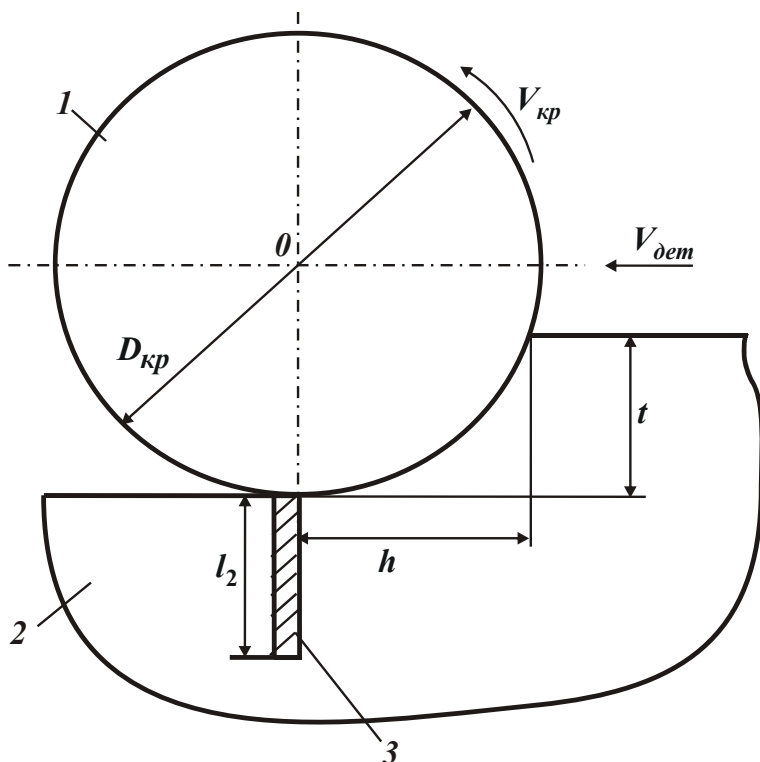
Расчетная схема плоского шлифования: 1 – круг; 2 – обрабатываемая деталь; 3 – адиабатический стержень поверхностного слоя детали.
